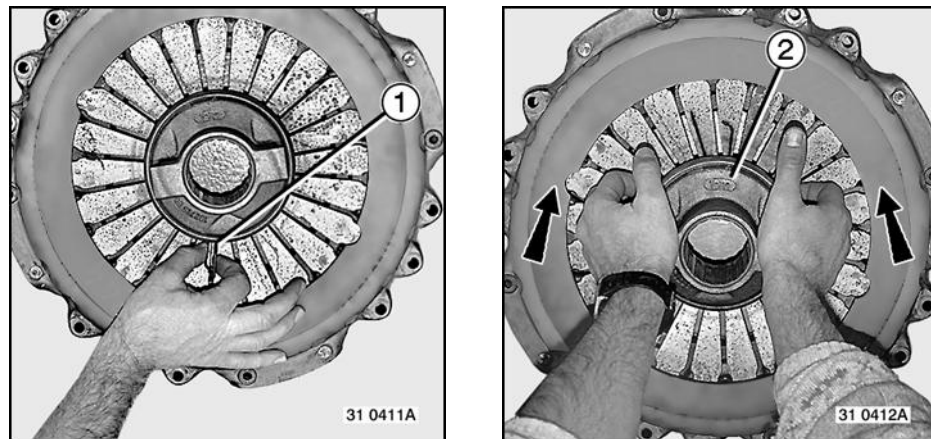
Вижимна вилка та самоцентрувальний вижимний підшипник у зборі
